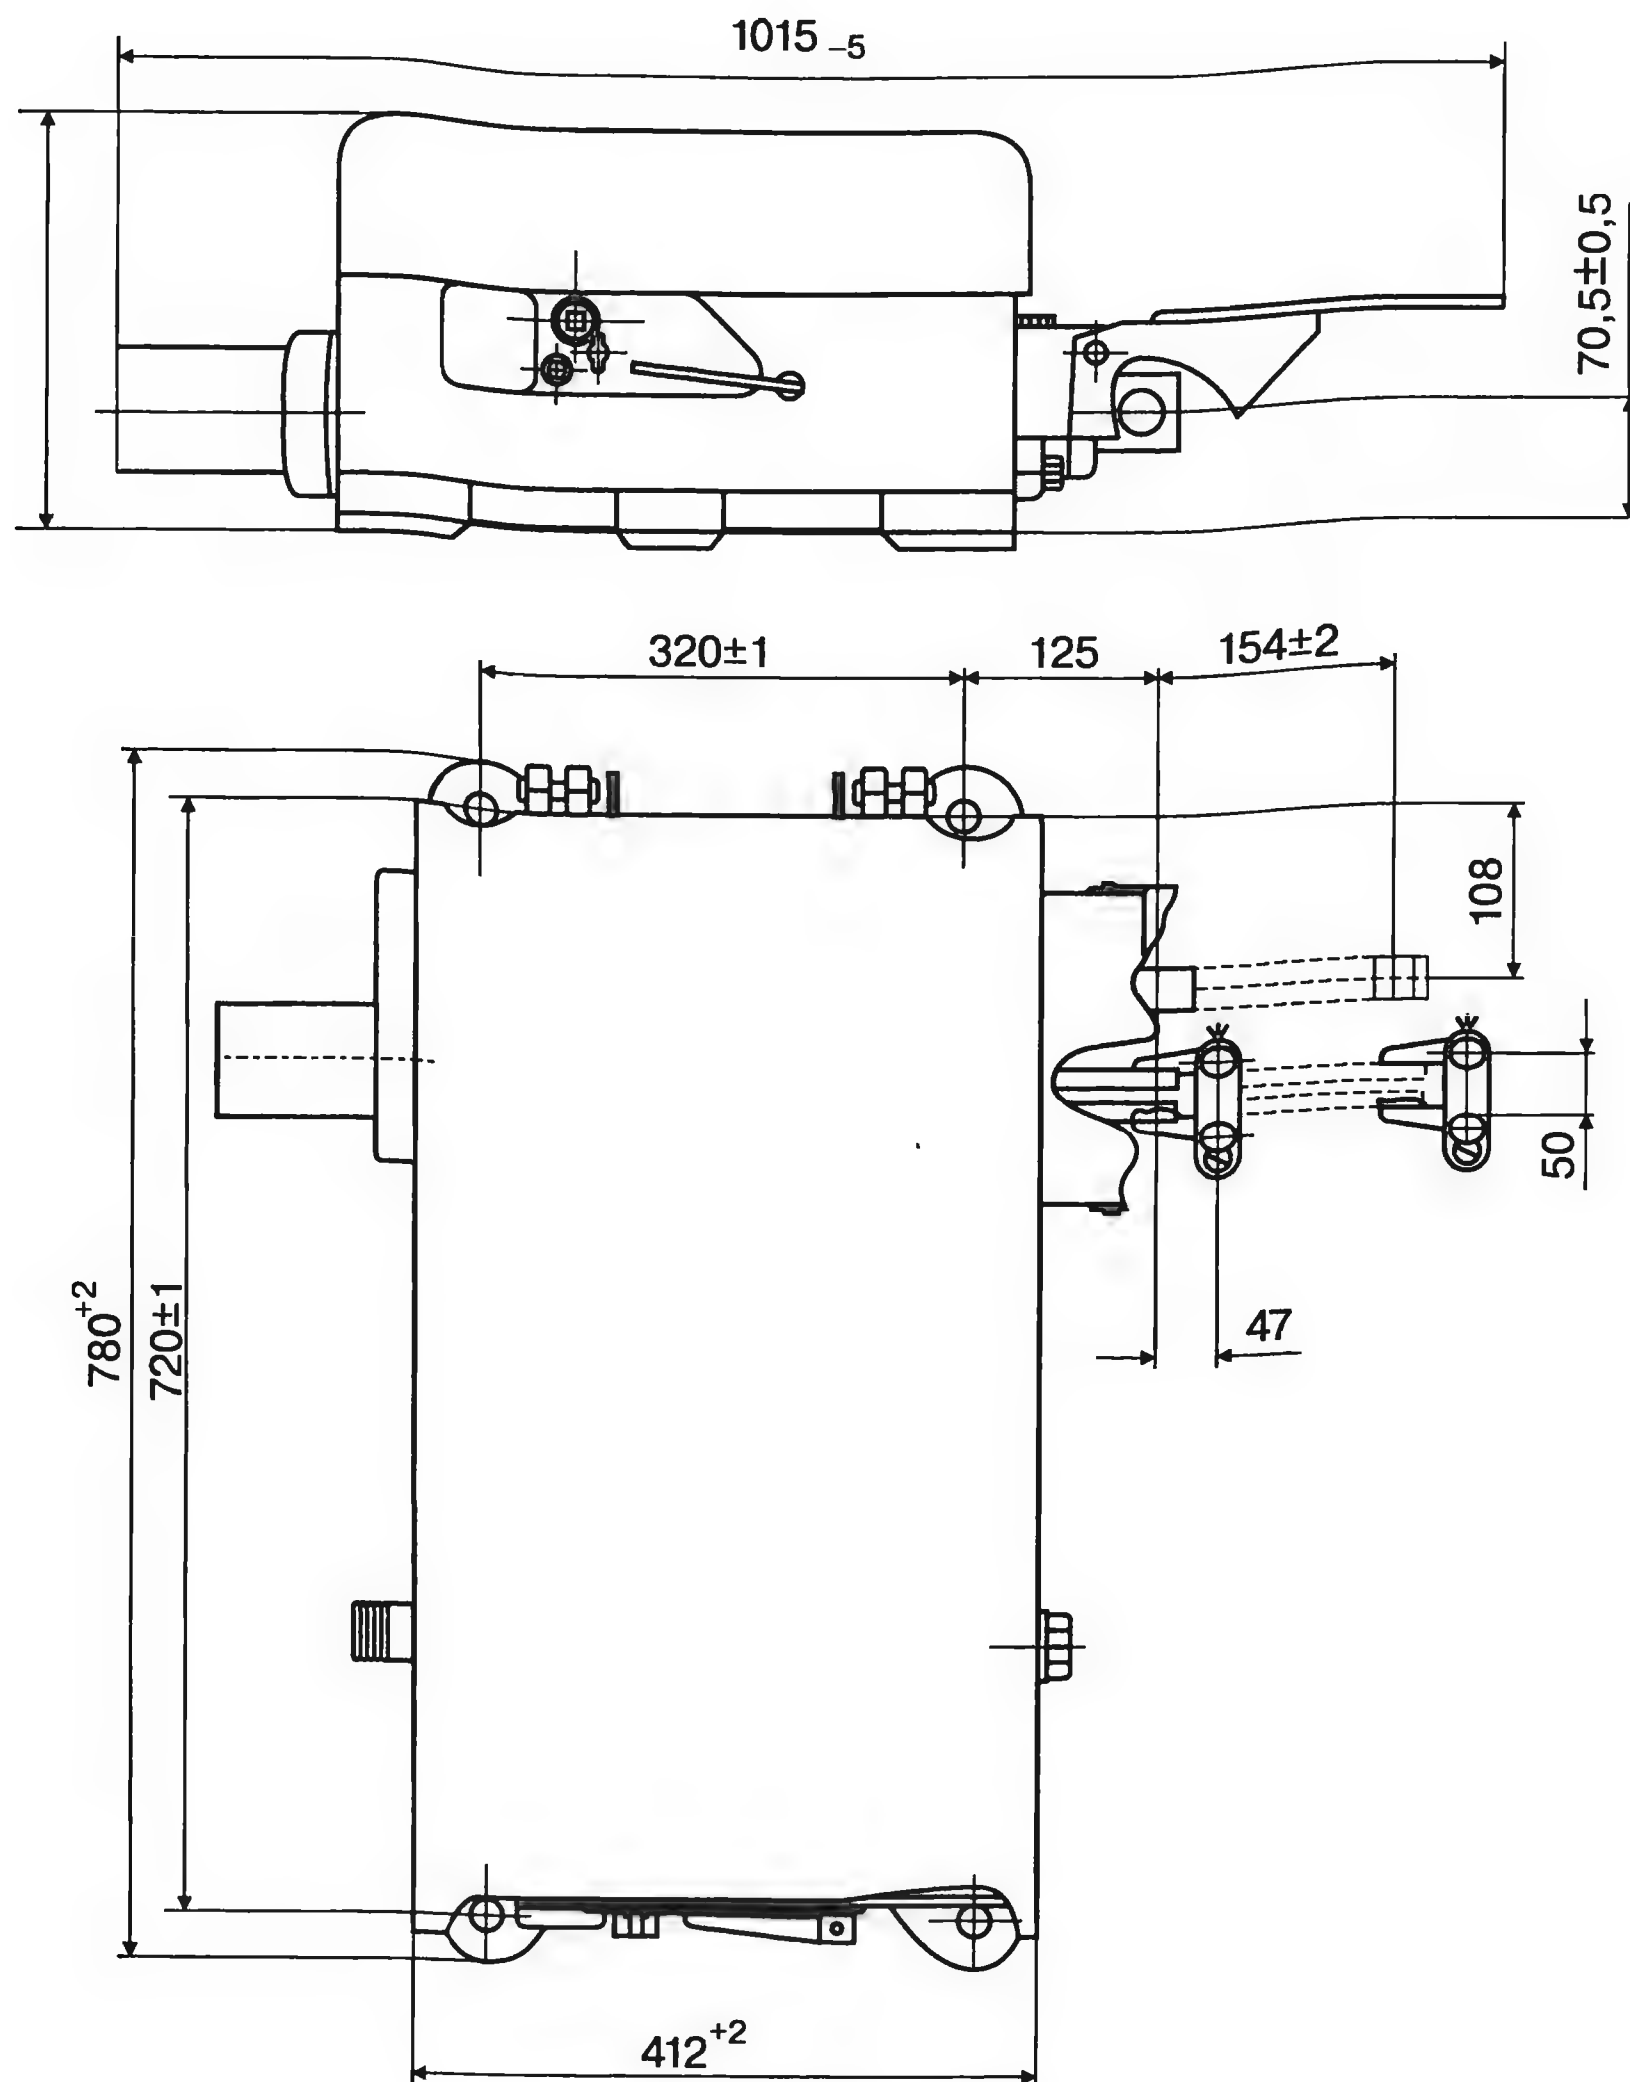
Габаритный чертеж электропривода типа СП-6К
